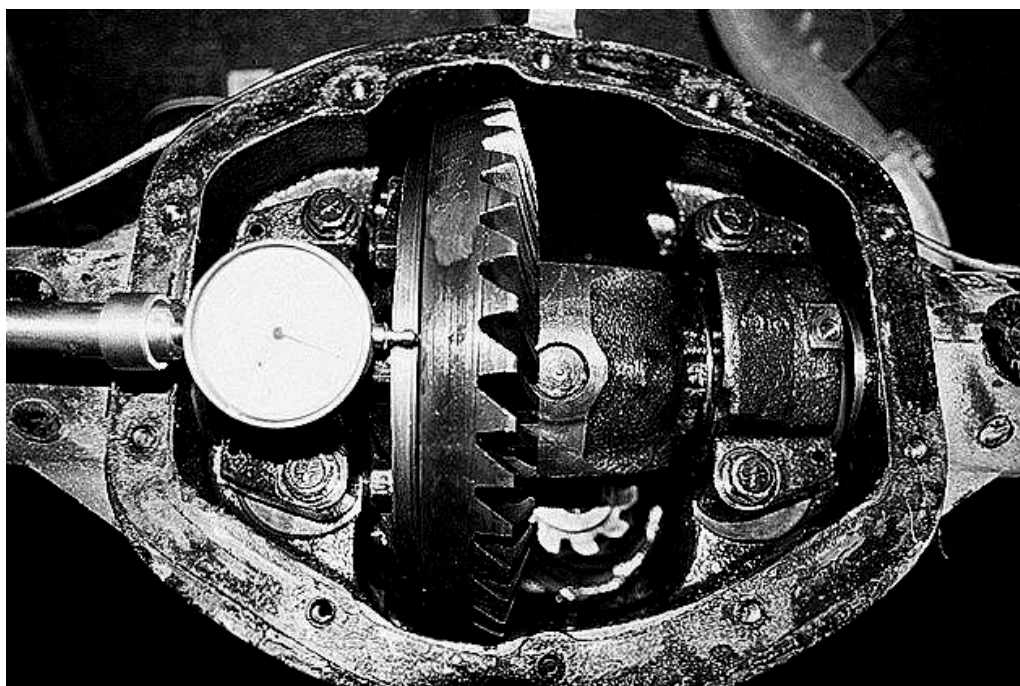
Измерение торцевого биения фланца корпуса дифференциала
